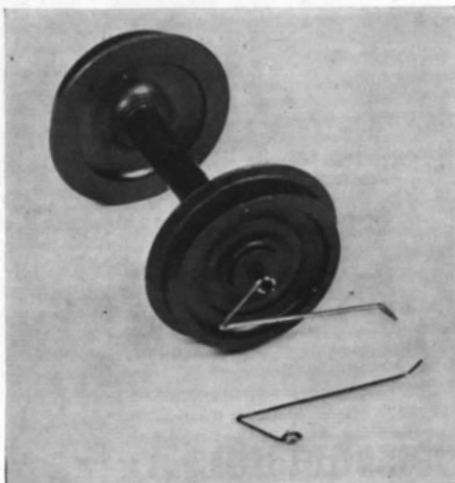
In dieser Form werden die „Minis“ aus 0,3 mm Federstahl Draht gebogen, wobei darauf zu achten ist, daß die Ose für die Achsführung nicht zu eng wird.
